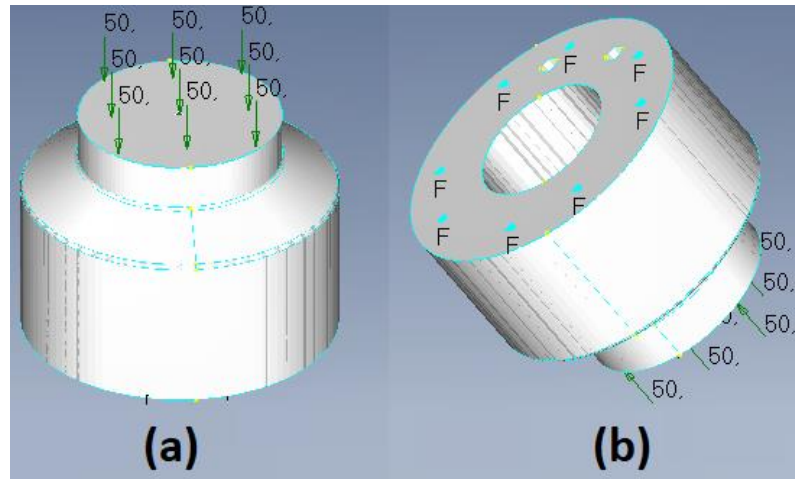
Aplicação de pressão em (a) e constrangimento de fixação em (b).
